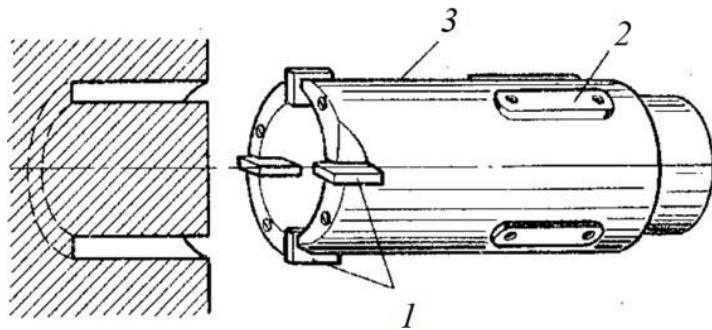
Приклад конструкції кільцевого свердла [29]
